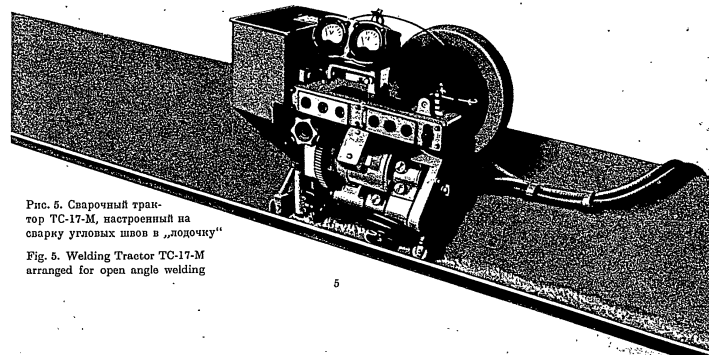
Сварочный трактор TC-17-M, настроенный на сварку угловых швов в „лодочку“
